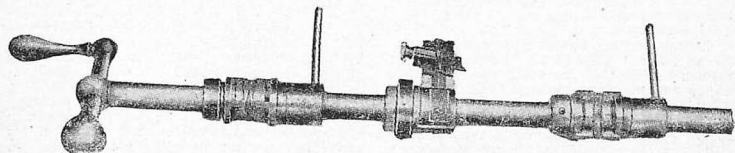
Инструмент с резцами для обточки поверхности подшипников
